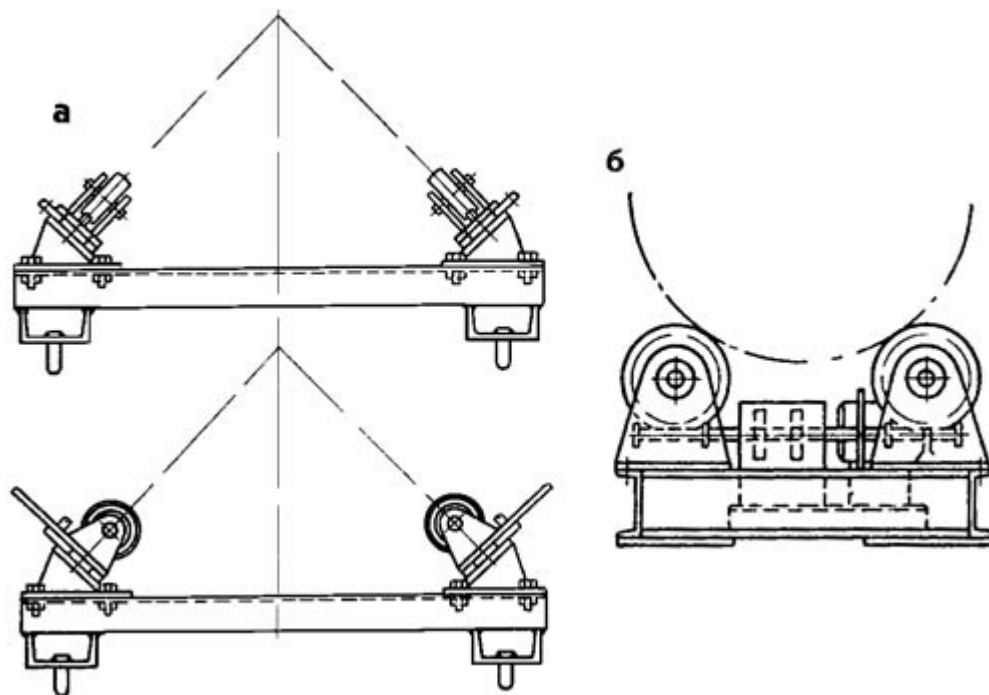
Роликові кантователи для складання і зварювання циліндричних обичайок.
